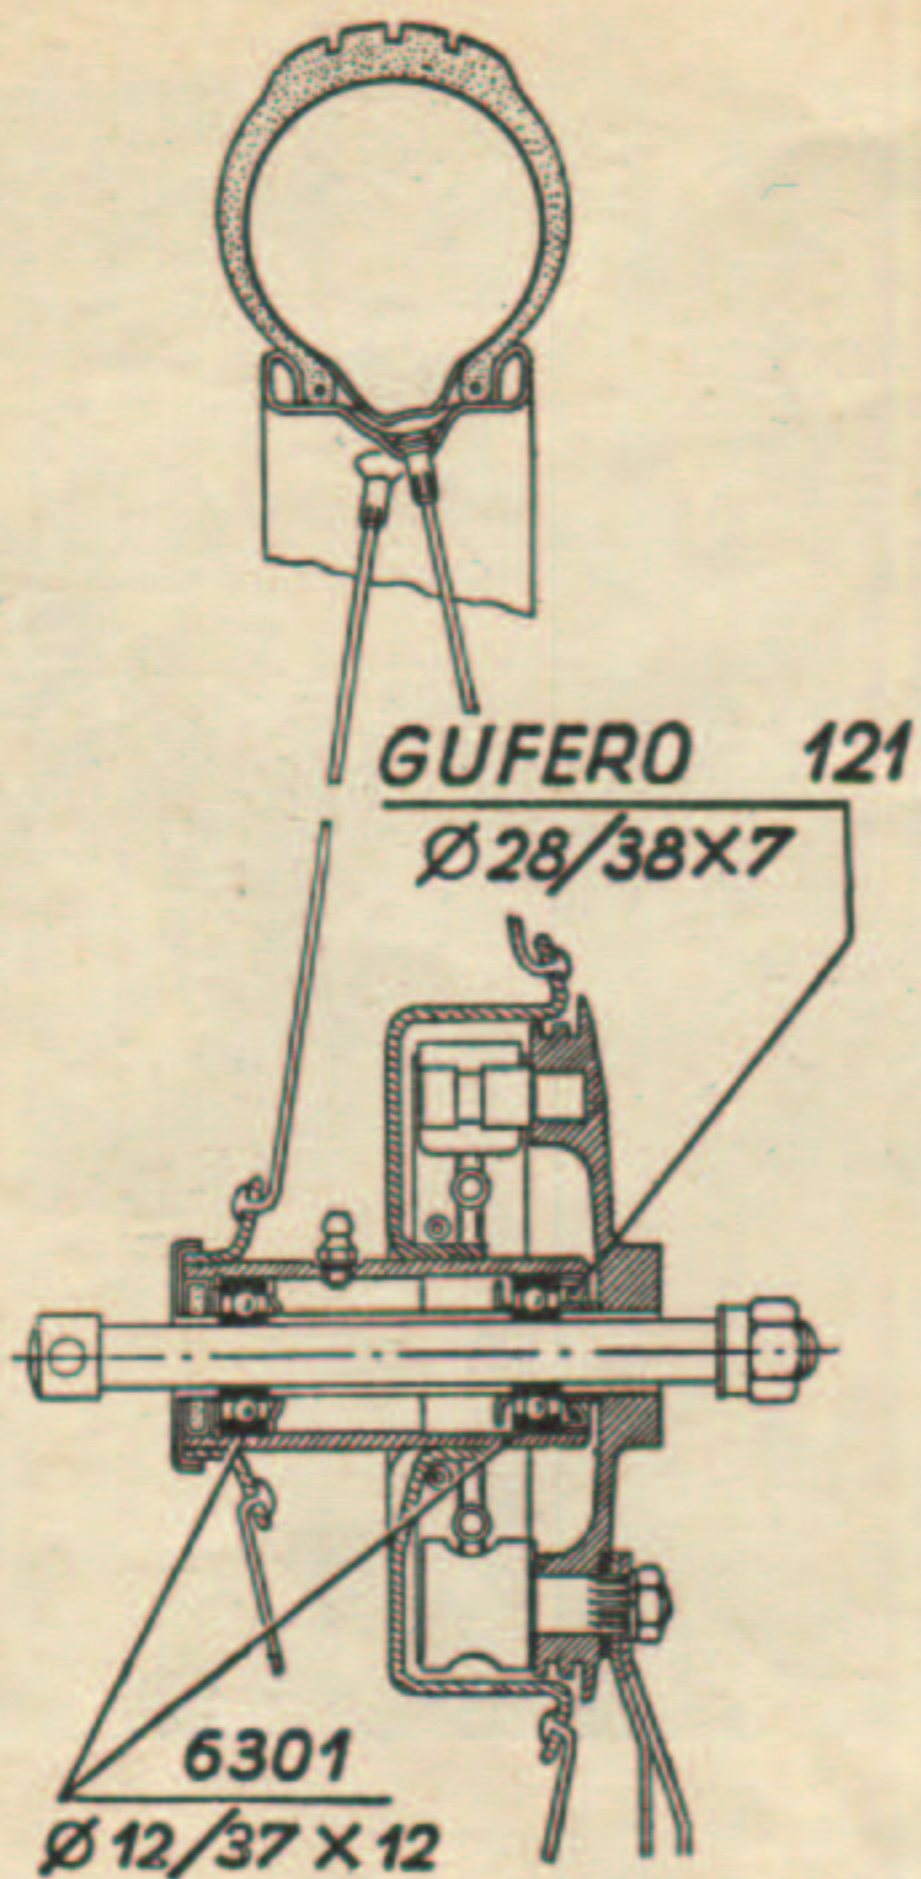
Vorderrad, alte Ausführung (im Schnitt)
